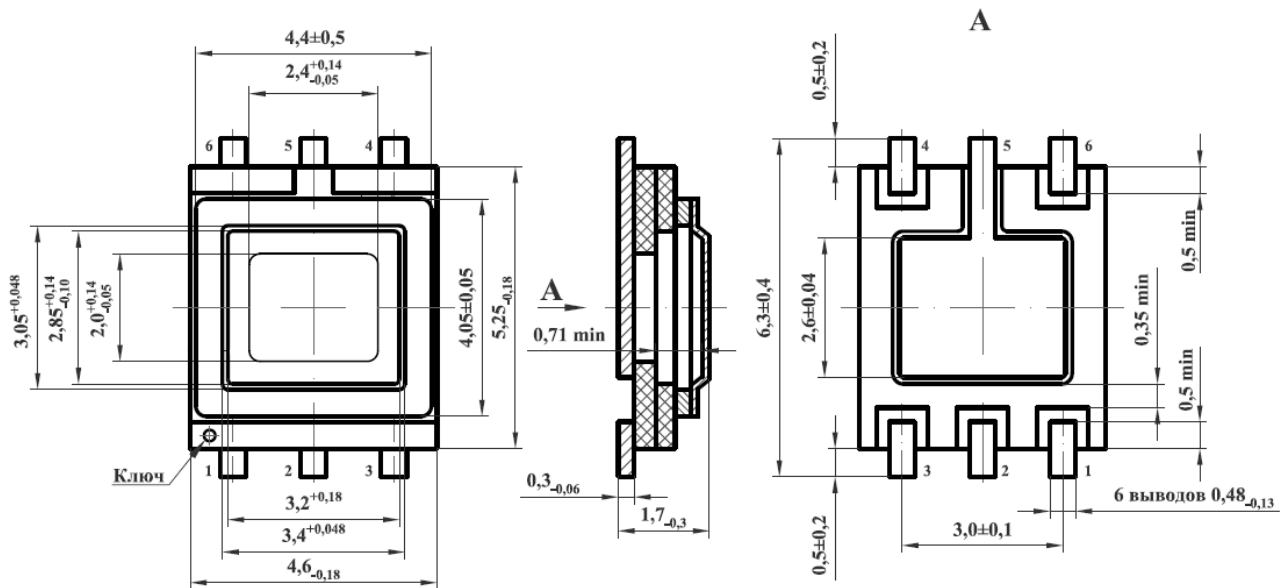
Габаритный чертёж корпуса 5221.6-1 (размеры в мм)
